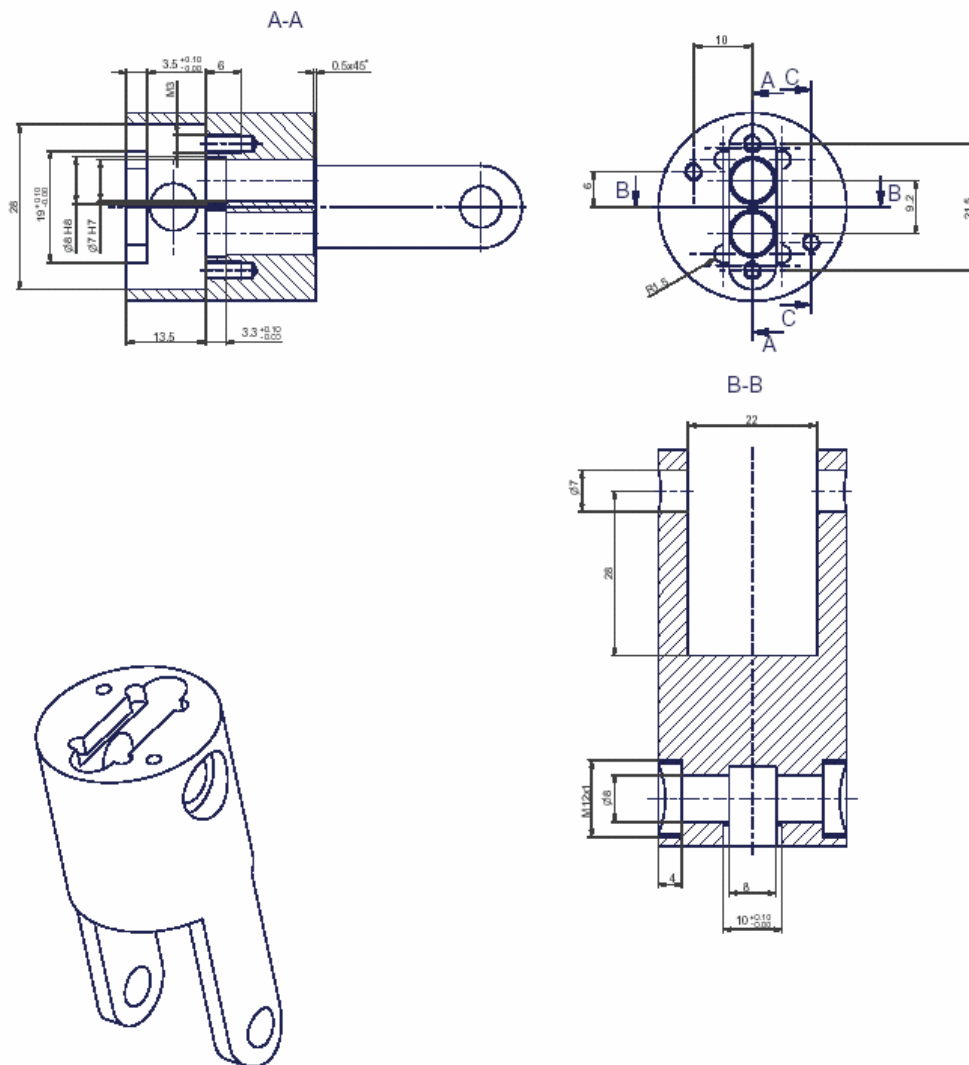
SOPORTE. VISTA DE PLANTA Y CORTES
